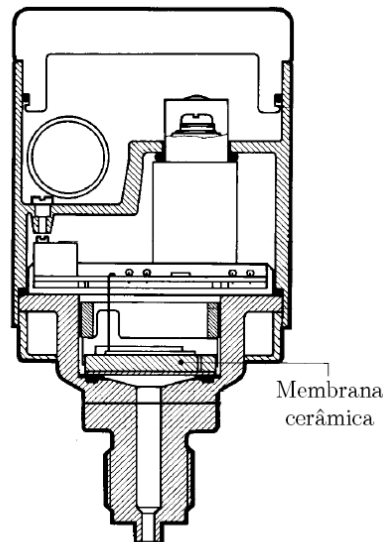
Vista em corte de ENDRESS HAUSER PMC133. (adaptado de [28])
